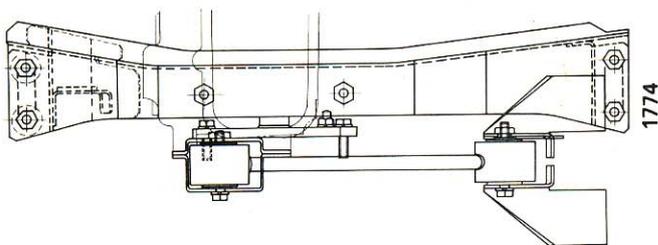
Sospensione gruppo motopropulsore per vetture
